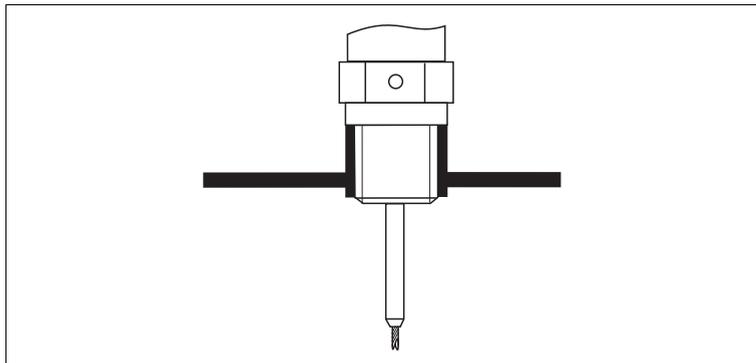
Montage mit Einschraubgewinde; bündig mit der Behälterdecke
